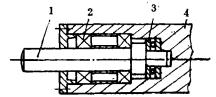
Accu-Roll穿孔机推入机推头结构 1一推头 2一滚动轴承 3一止推轴承 4一推杆体
